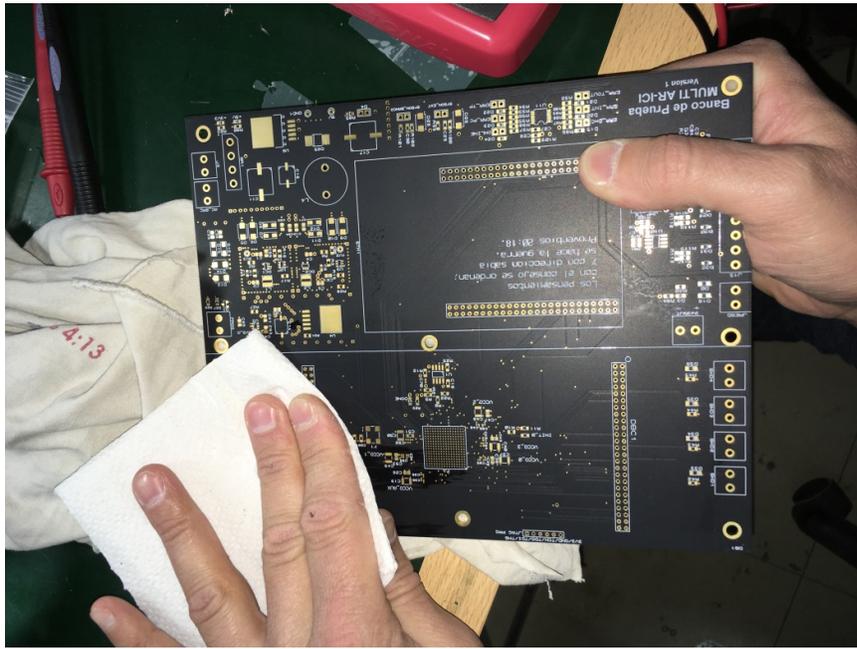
Limpieza preliminar de la zona de soldadura.
